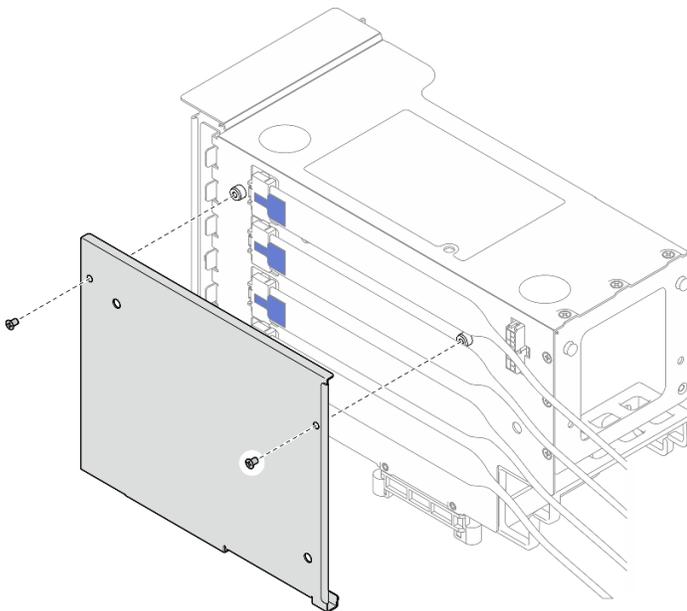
Installation du cache sur le boîtier de la carte mezzanine
